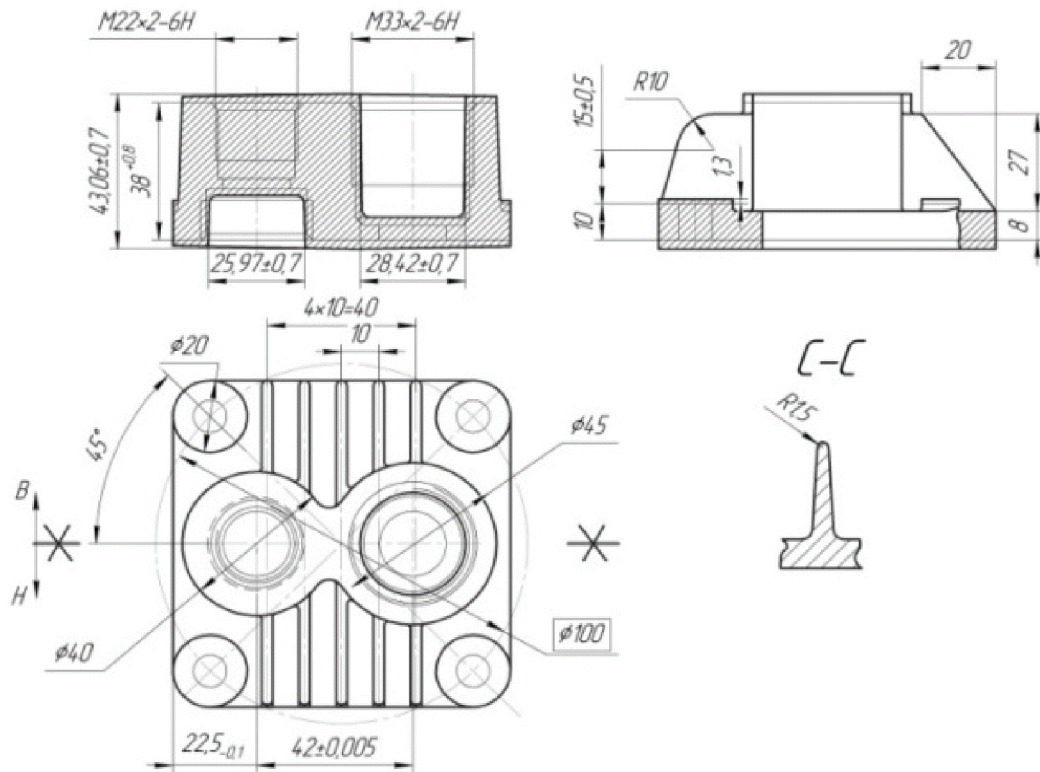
Ескіз заготовки для деталі «Корпус 21.10» (лиття)
